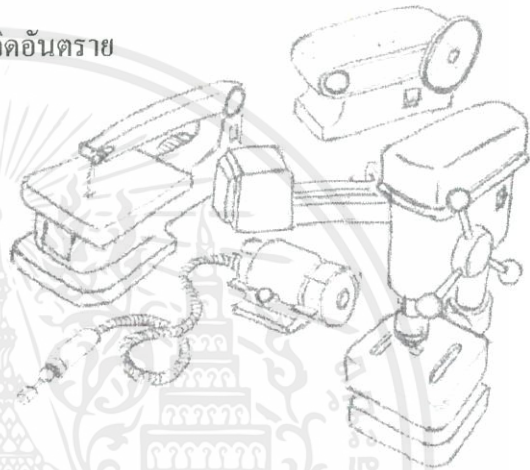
เครื่องมิลลิ่งขนาดเล็ก (SMALL MILLING MACHINE)
